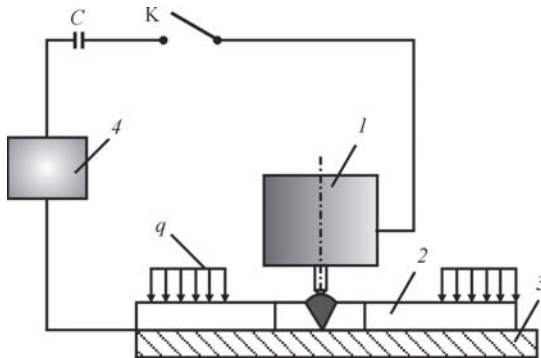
ЭДО образцов сварных соединений сплава АМгб при «жестком» закреплении: C — емкостной накопитель энергии; K — силовой ключ; q — фиксирующая нагрузка; 1 — ЭУ; 2 — образец; 3 — сборочная плита; 4 — датчик Холла
